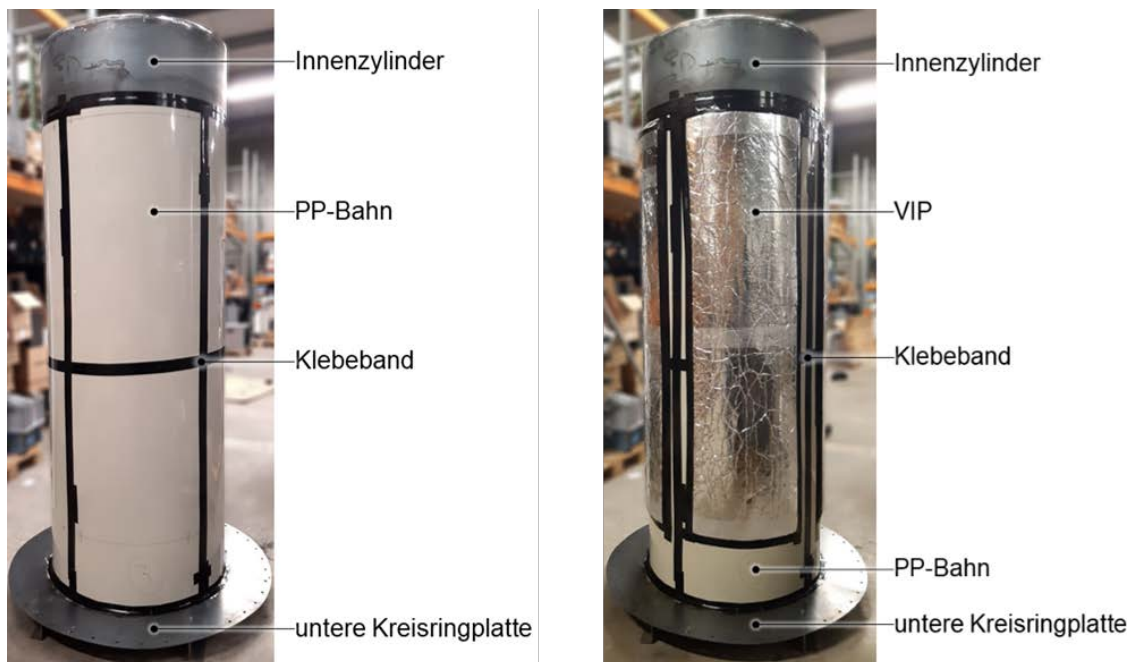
Innenzylinder des Formwerkzeugs für die Manteldämmung der Wärmedämmung 2 mit PP-Bahnen (links) und VIP aufgeklebt auf die PP-Bahnen (rechts)
